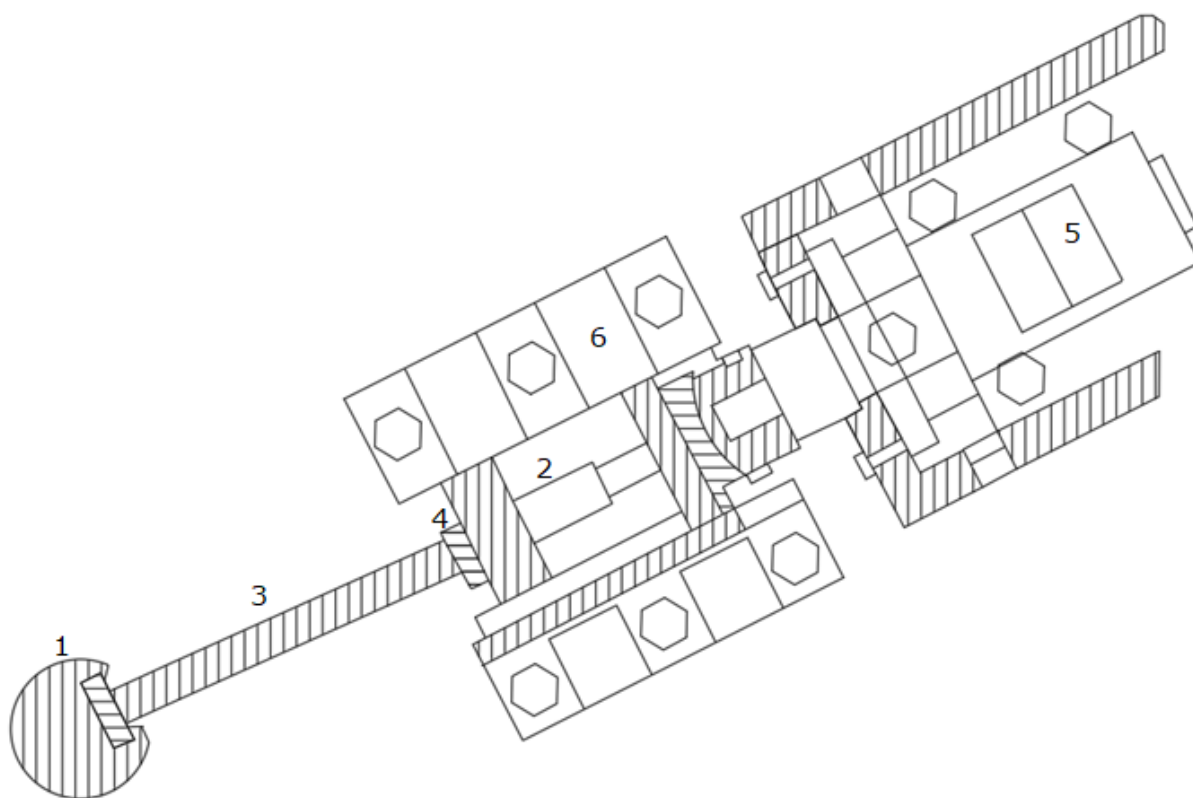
Схема регулювального механізму 1 – підшипник, 2 – два допоміжних гідроциліндри, 3 – пластина, 4 – передня накладка, 5 – головний гідроциліндр, 6 – корпус
